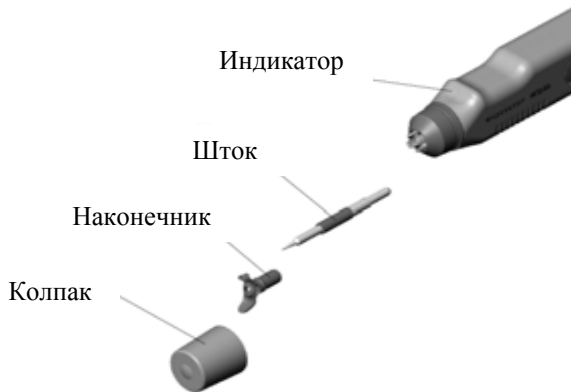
Подготовка индикатора к очистке штокового механизма
